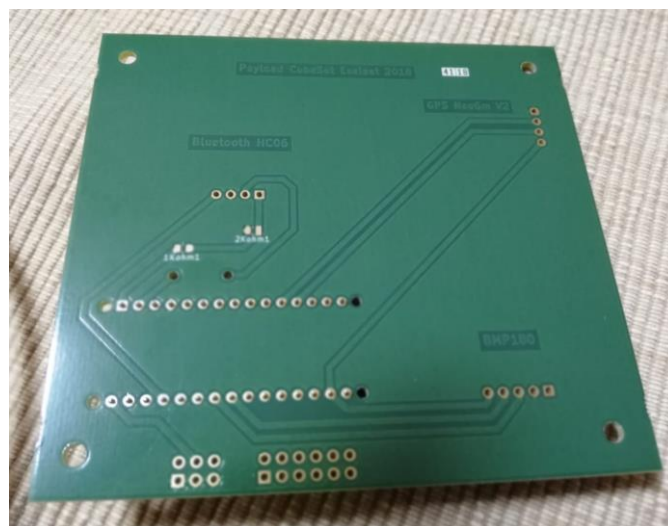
Placa PCB recibida pendiente de soldar componentes y de modificaciones
